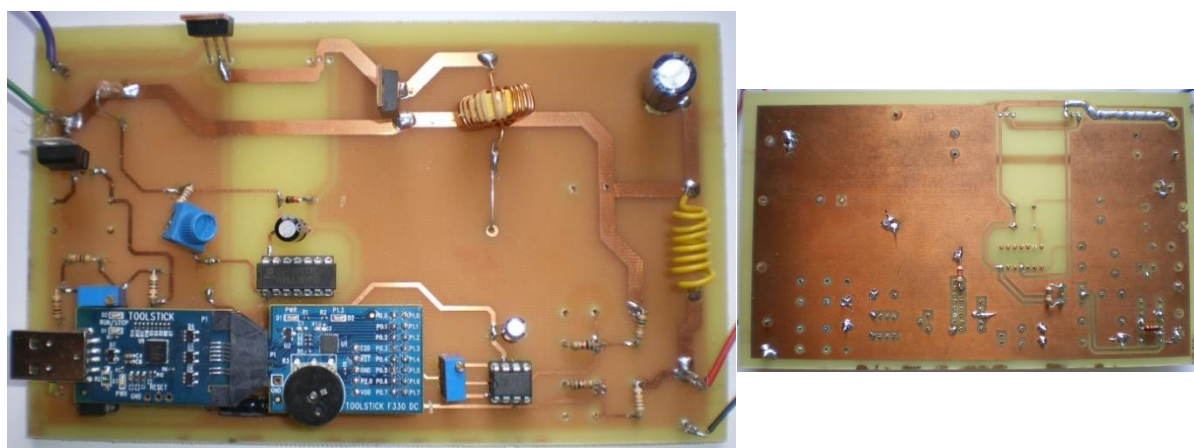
Imágenes del resultado final de la PCB (top-izquierda y bottom-derecha).
